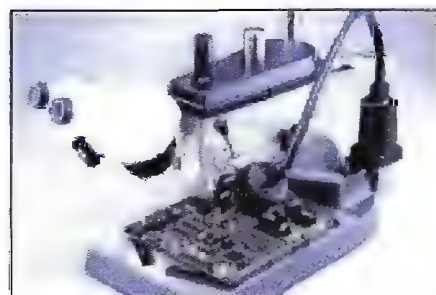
Прецизионный сверлильный станок с рабочим столом
